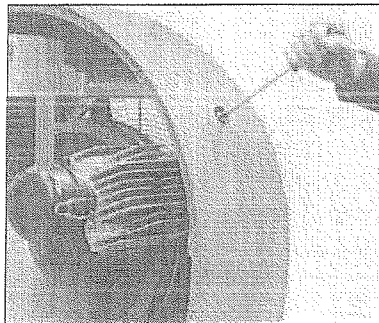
Крепежные винты кожуха охлаждающего воздуха
